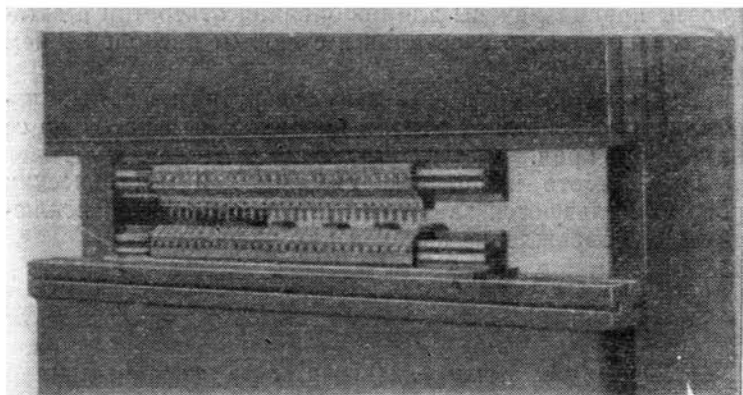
Гибочный пресс для пробивания отверстий с многоштемпельным инструментом
